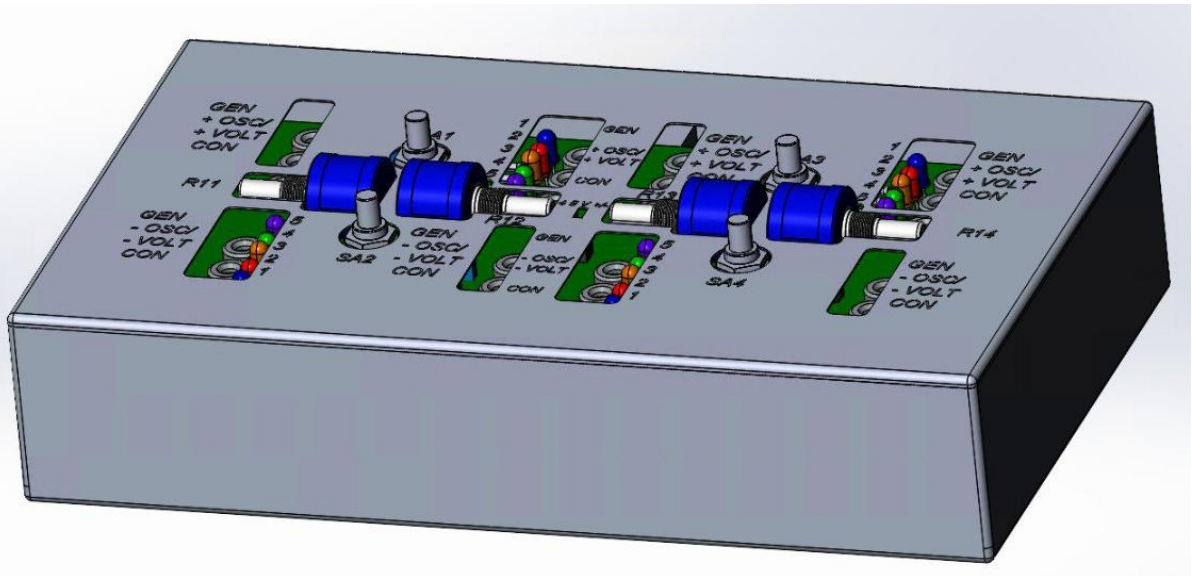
Вигляд зібраного корпусу лабораторного макету
